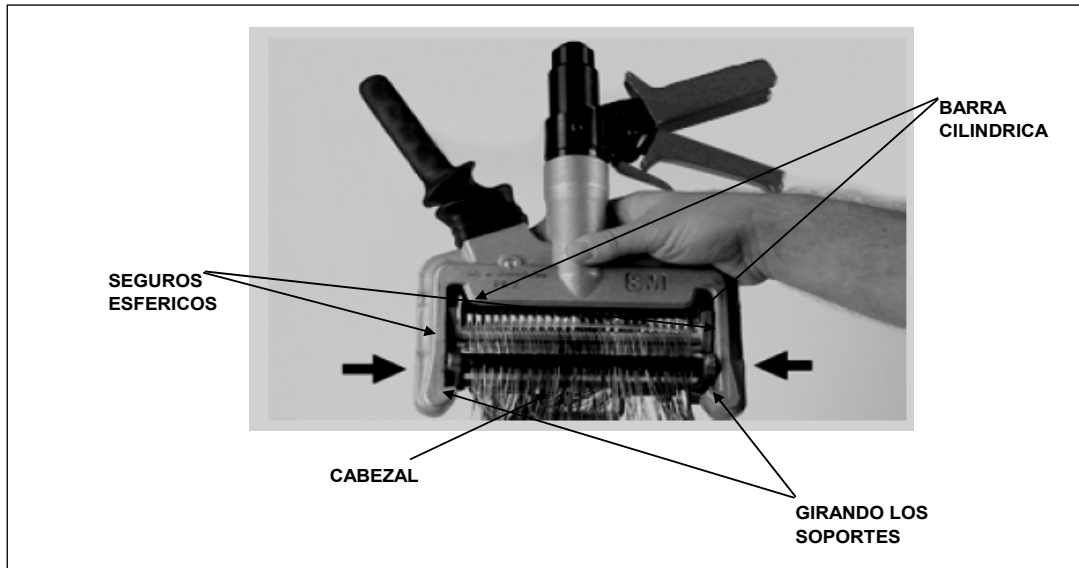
Montaje de la Mini Prensa Hidráulica.
